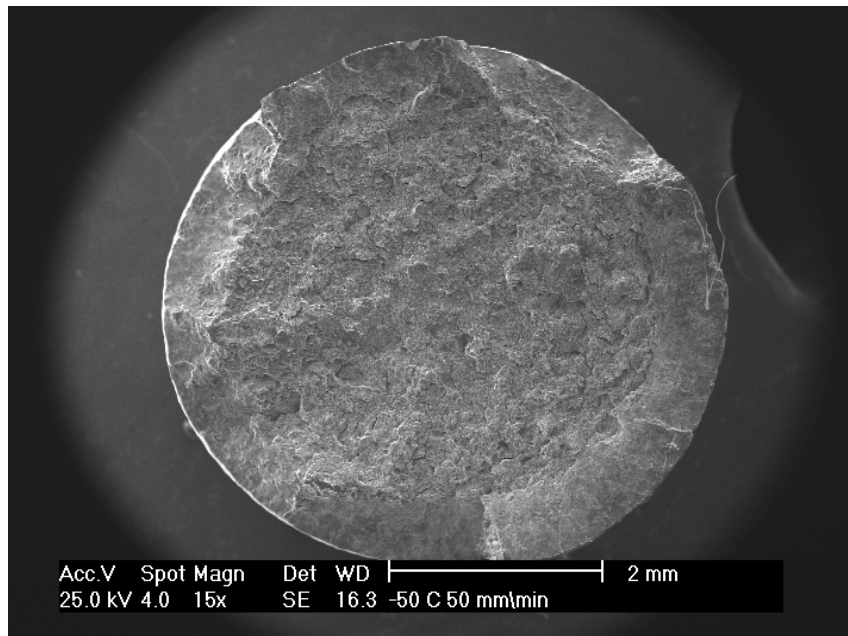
a: Superficie fracturada de la sección transversal de la probeta
